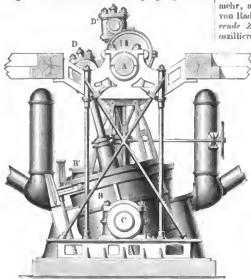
Oszillierende Zwillingschiffsmaschine.
